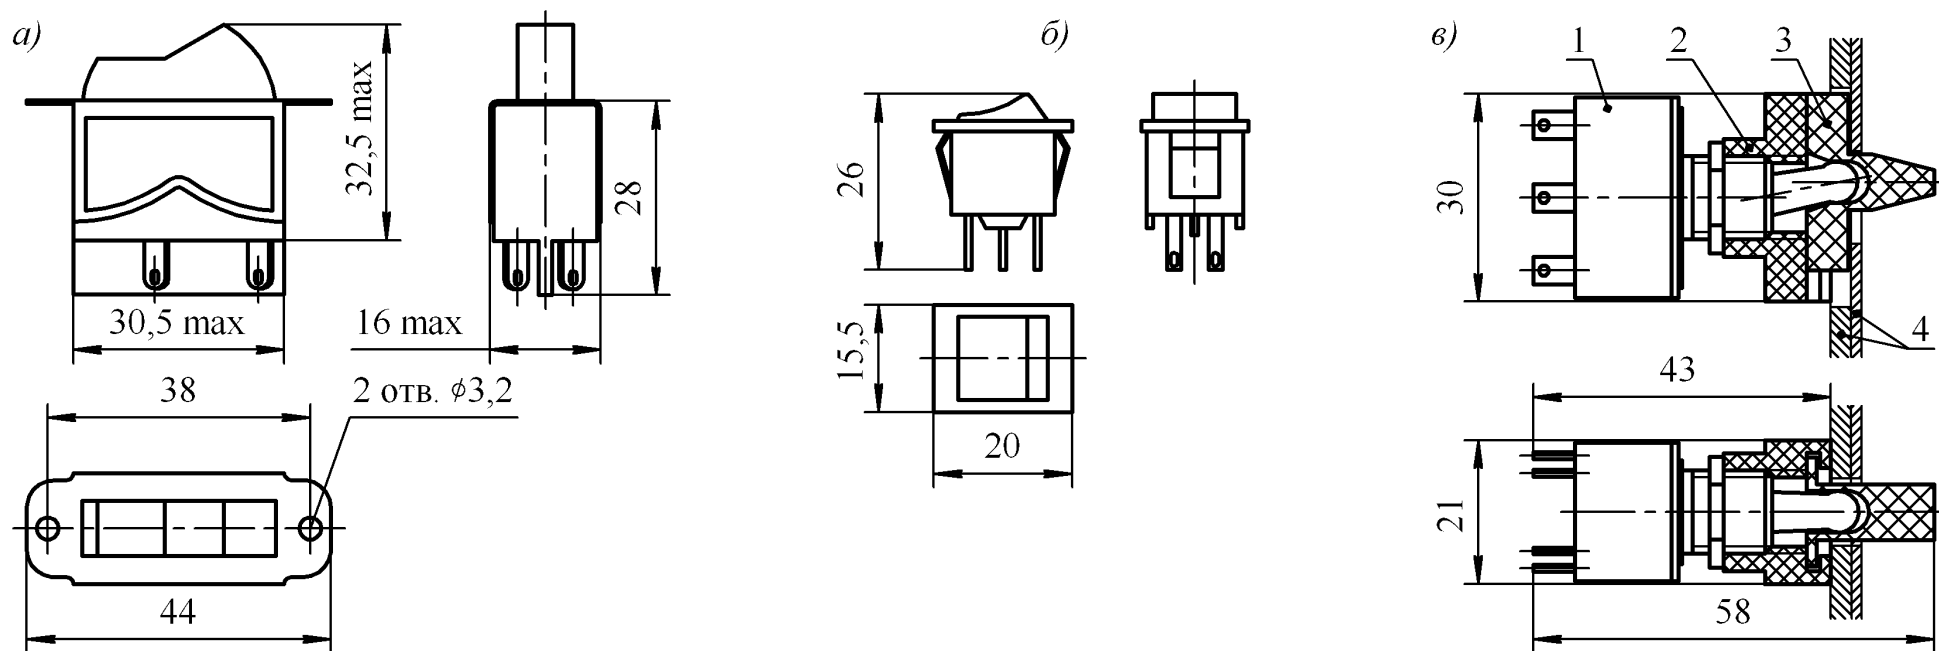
Примеры сетевых выключателей. 1 – тумблер ТЗ, 2 – пластмассовый корпус, 3 – пластмассовый движок, 4 – доступные металлические части прибора
